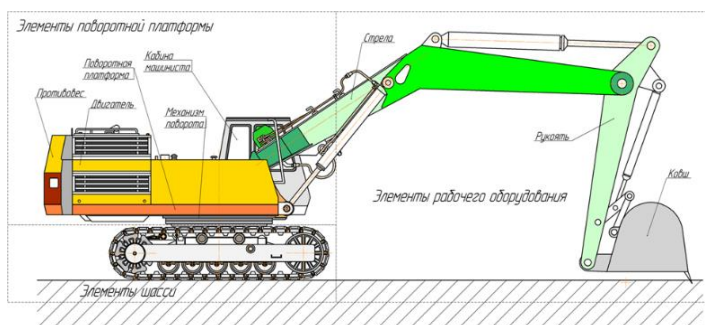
Основные части одноковшового карьерного гидравлического экскаватора
